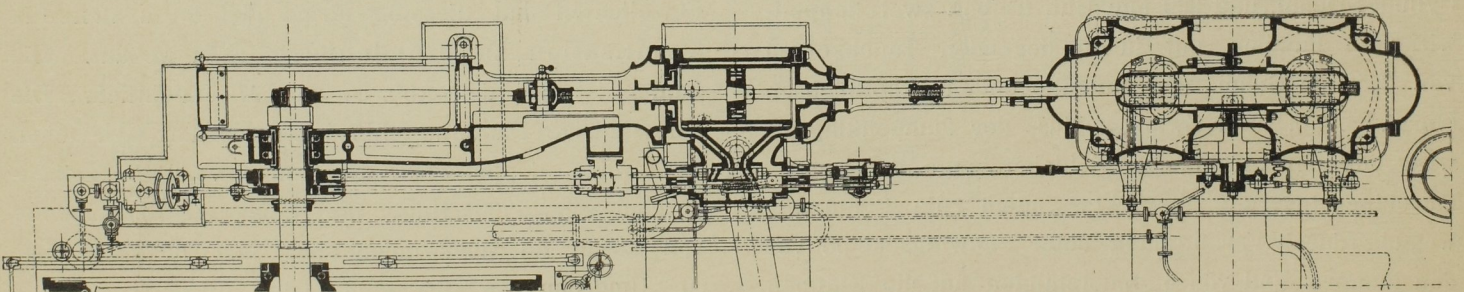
Seitenansicht und Grundriss. Masst. 1:50.
